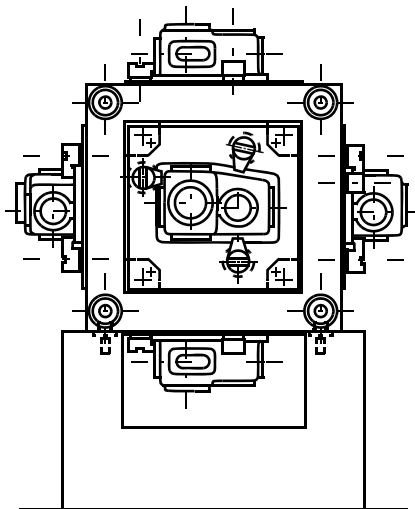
Автоматический сменный модуль — носитель призматической формы для базирования и крепления обрабатываемых деталей, приспособлений, исполнительных механизмов
